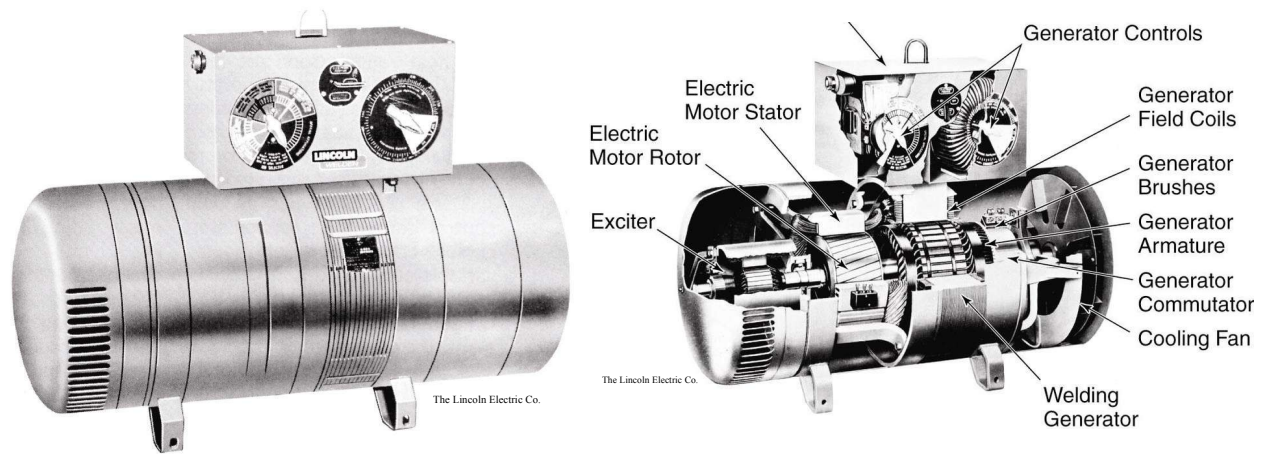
Générateur de soudage à base d'une génératrice DC
